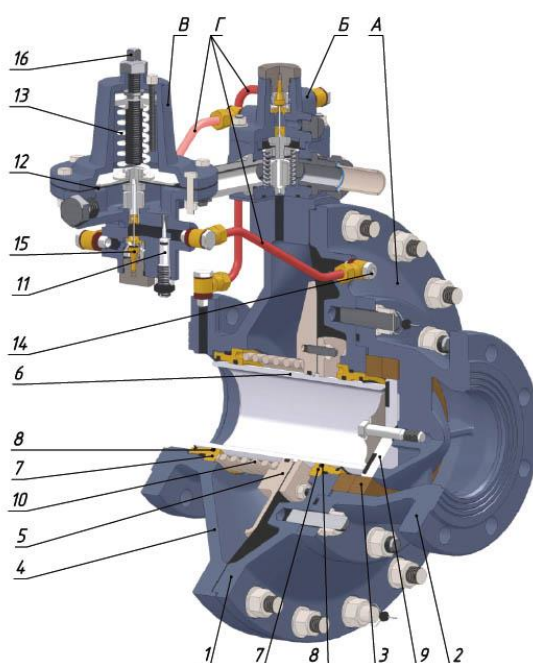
Устройство РДП-50В: А – исполнительный механизм; Б – стабилизатор (у регулятора с высоким давлением отсутствует); В – пилот (регулятор давления); Г – соединительные трубопроводы; 1 – крышки; 2 – фланец переходник; 3 – шумоглушитель; 4 – корпус; 5 – подвижная система мембранного типа; 6 – тонкостенная гильза; 7 – направляющие; 8 – уплотнительные кольца; 9 – клапан с эластичным уплотнителем; 10 – пружина; 11 – регулируемый дроссель сбросной линии; 12 – мембрана; 13 – пружина; 14 – регулируемый дроссель; 15 – клапан пилота; 16 – винт
